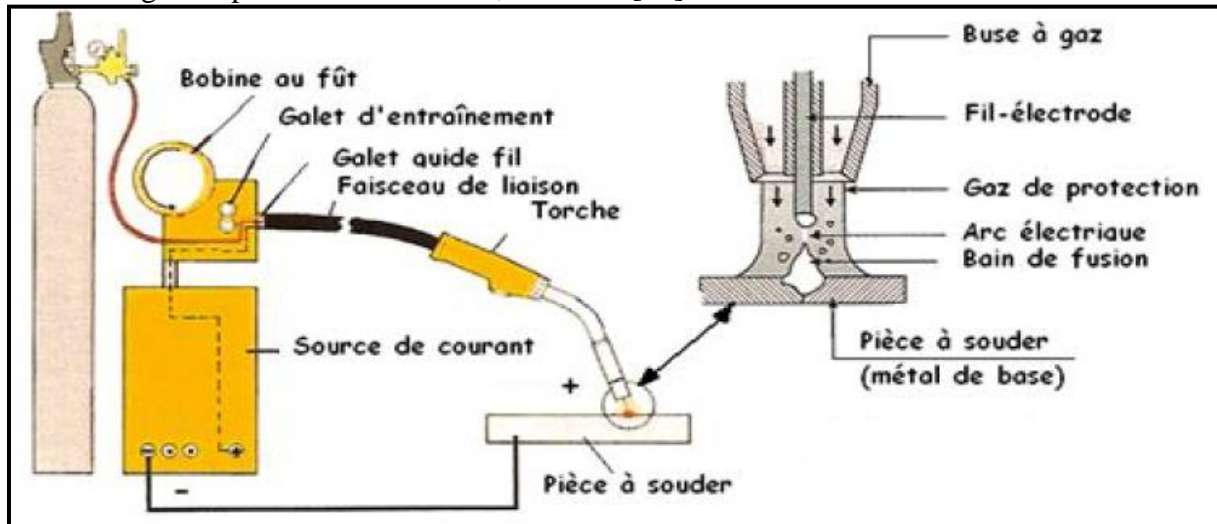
Principe de la procédé du soudage MIG/MAG [31].
